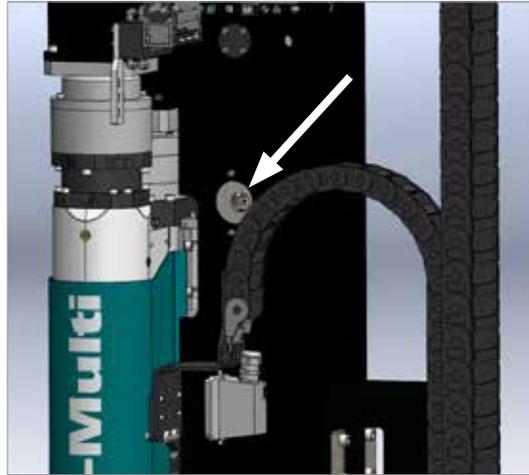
Seitenansicht (senkrecht) mit Schmierpunkten der Kugelgewindespindel des Schlittens (Schlitten 130 mm unterhalb der voll ausgefahrenen Position)
